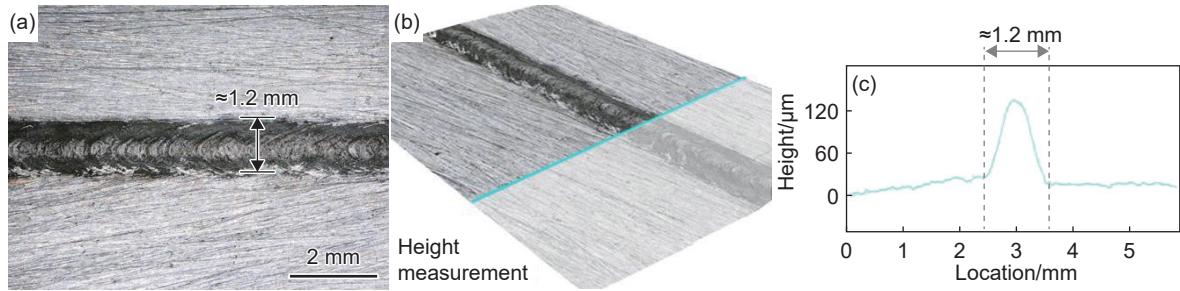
焊缝宏观形貌 (a) 焊缝形貌; (b) 焊缝三维形貌; (c) 焊缝轮廓曲线
